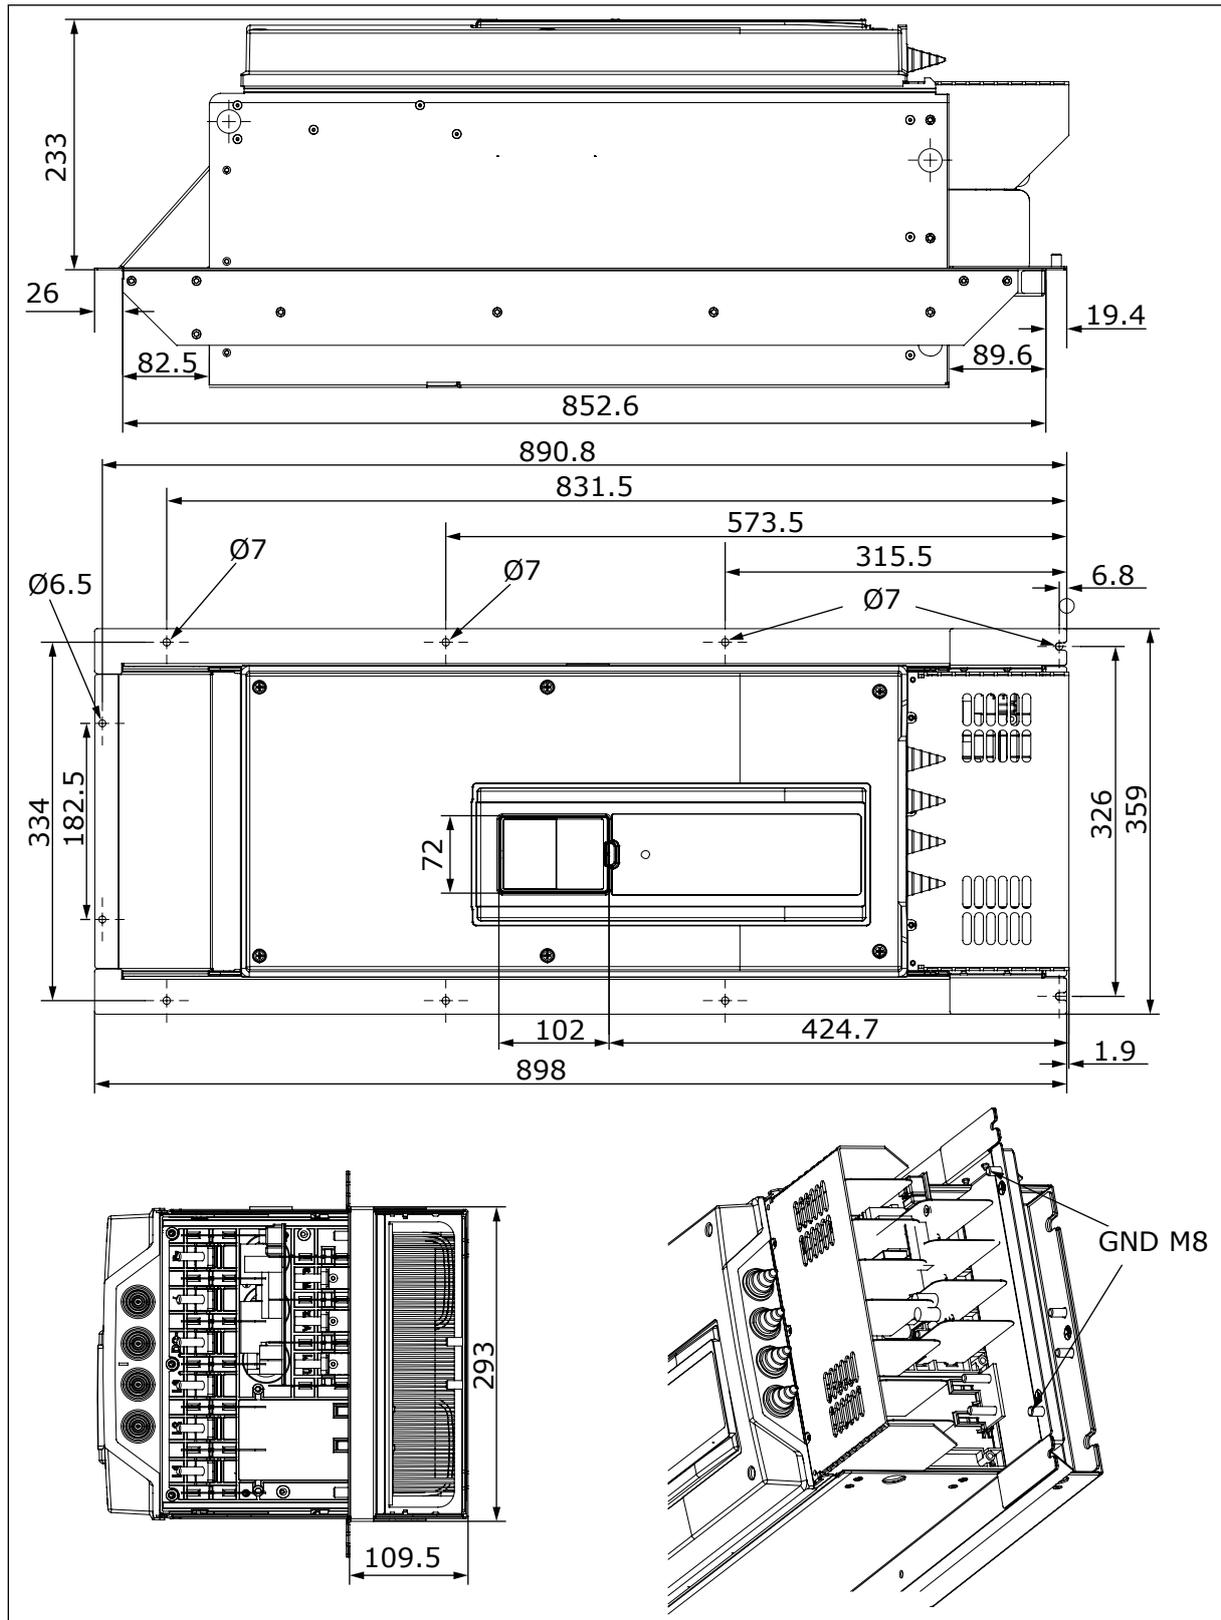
Abmessungen des Frequenzumrichters, Flanschbefestigung, MR8 [mm]
